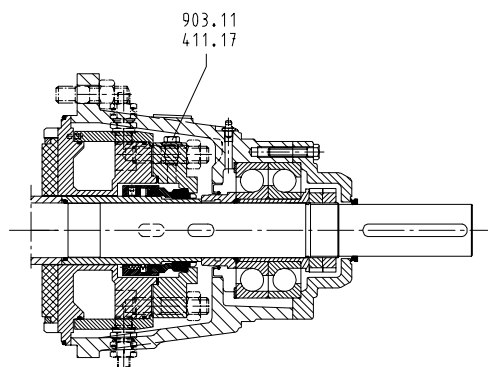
Резьбовая пробка отверстия для удаления воздуха уплотнительной камеры (уплотнительная камера с водяным охлаждением) - типоразмер с 125 по 150 (и при необходимости для типоразмеров 32-100 как специальное оборудование)
